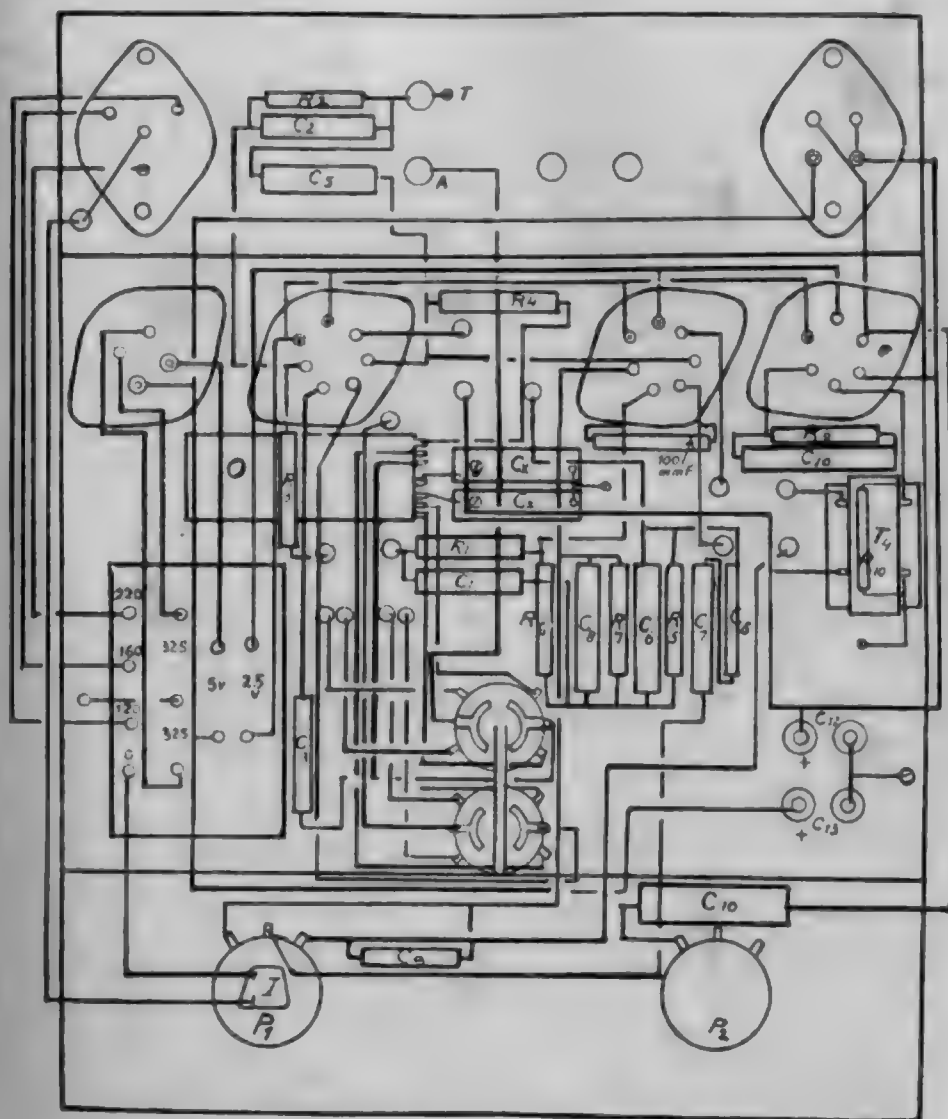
Piano di costruzione dell'apparecchio M 3.
